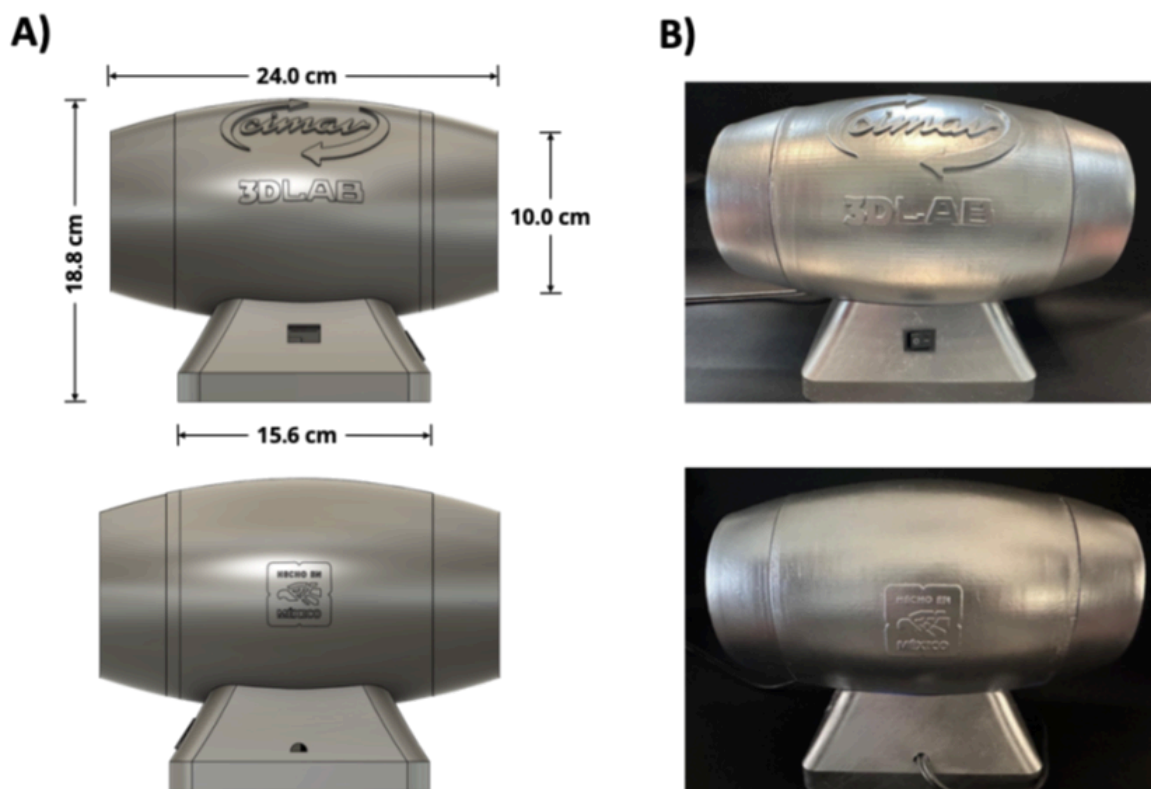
A) Diseño CAD del Sistema de desinfección fotocatalítica. B) Sistema impreso y completamente ensamblado.
